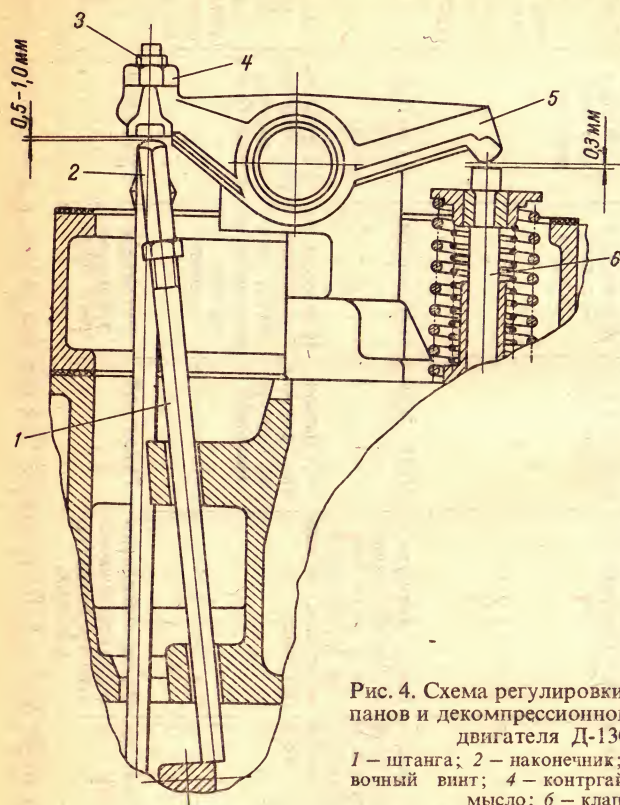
Схема регулировки зазоров клапанов и декомпрессионного механизма двигателя Д-130Т:
